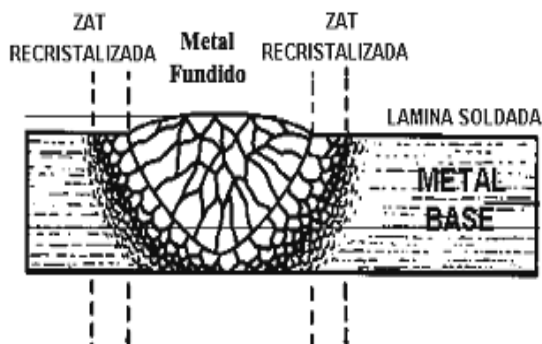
Esquema de las zonas involucradas en un cordón de soldadura. Fuente: SAGER S.A. (2004).
